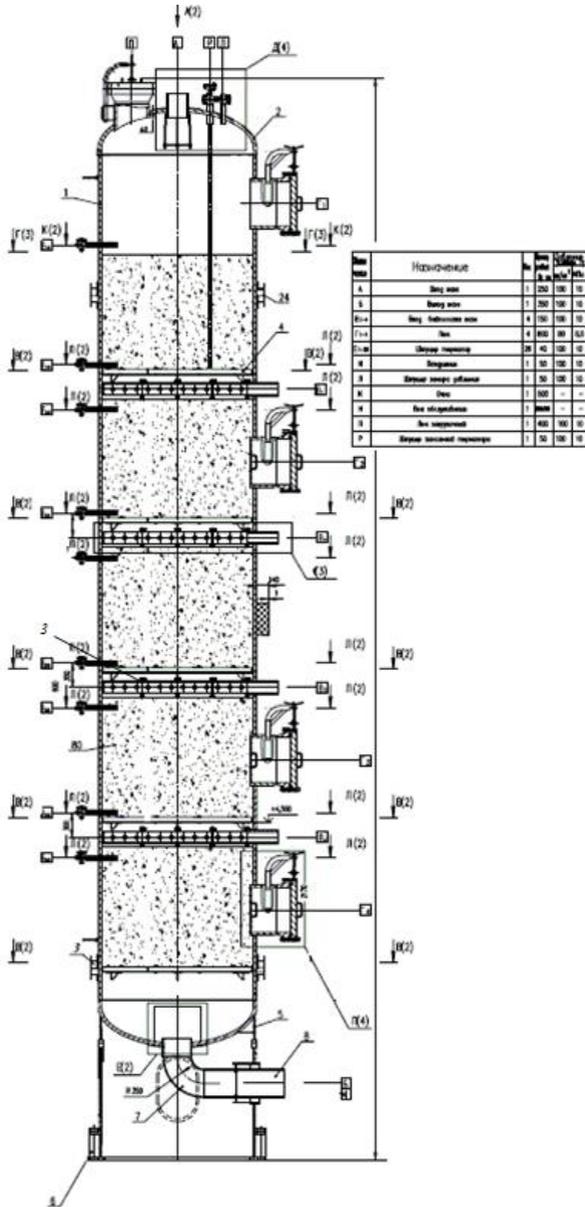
Конструкция адиабатического каталитического реактора с вводом байпасного охлажденного сырья: 1 – корпус; 2- днище; 3 -холодные байпасы; 4 - колосниковая решетка (полка); 5 – цилиндрическая опора; 6 – подкладной лист; 7 – смотровой люк; 8 – штуцер вывода продукта; 9– люки-лазы; 10 – катализатор; 11 – монтажные штуцера.
